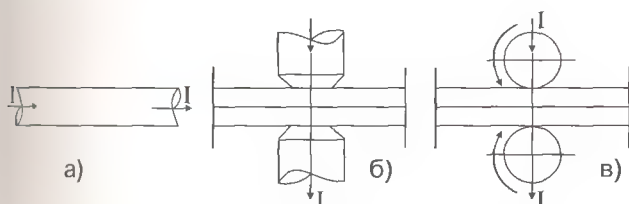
Основные разновидности контактной сварки
